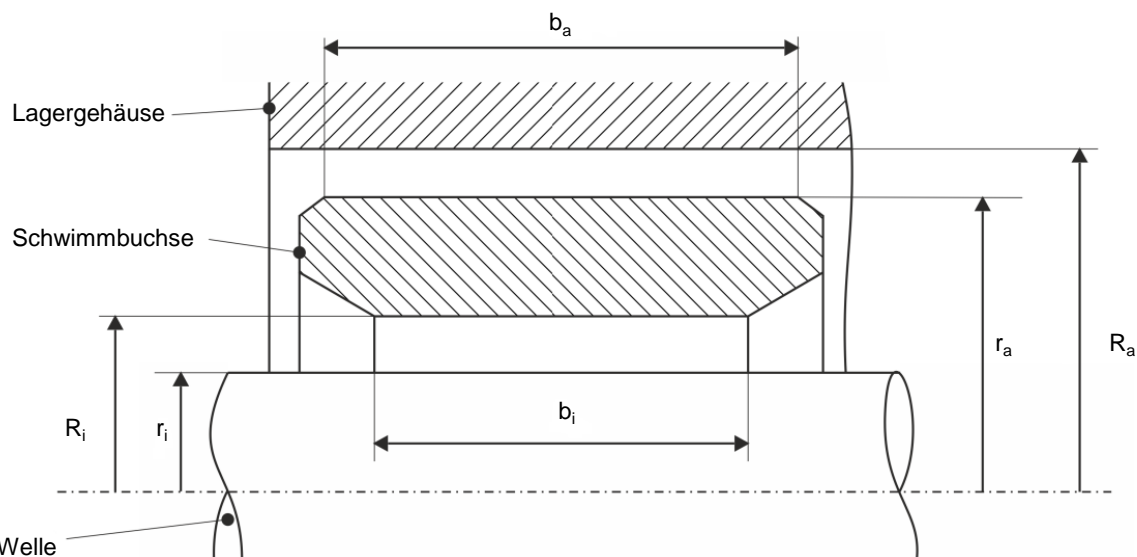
Geometrische Grundparameter der Schwimmbuchsenlagerung [41] mit Wellen- r_i und innerem Schwimmbuchsenradius R_i , sowie äußerem Schwimmbuchsen r_a und Gehäusebohrungsradius R_a und axialer Ausdehnung des inneren b_i und äußeren b_a Schmierfilms
